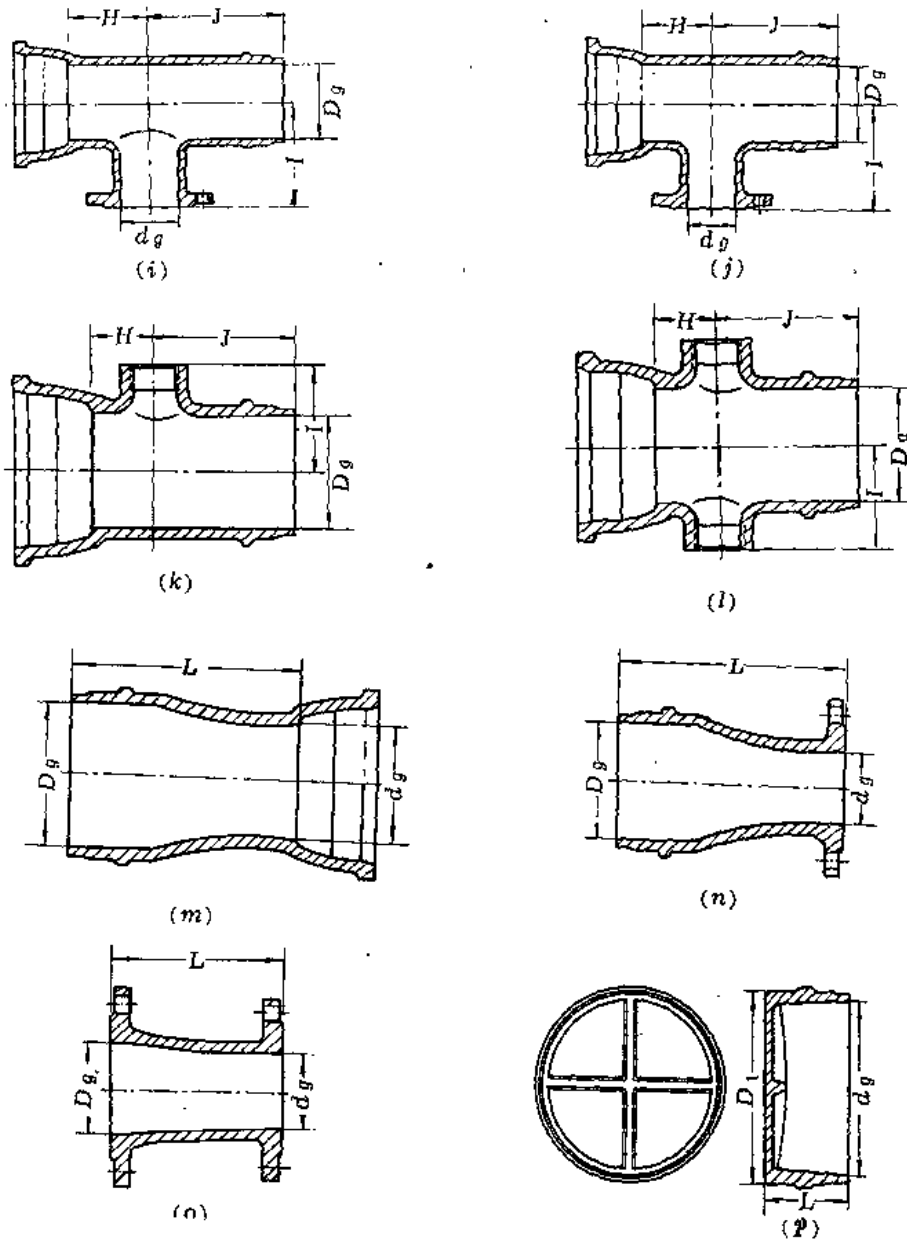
自应力钢筋混凝土管铸铁管件 (二)
